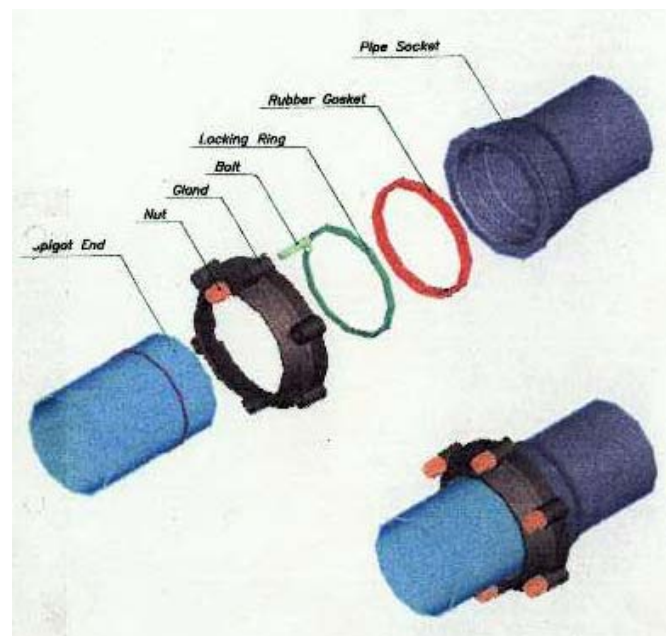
耐震離脱防止継手 (Anchor Joint)
